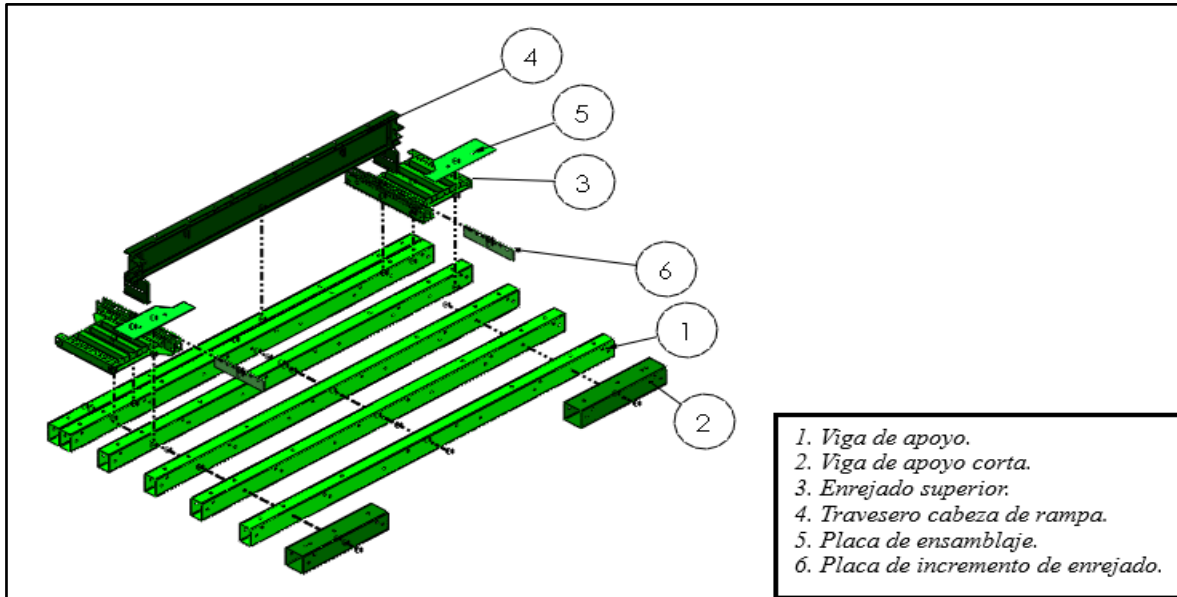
Vista explosionada cabeza rampa. Fuente: Elaboración propia.
